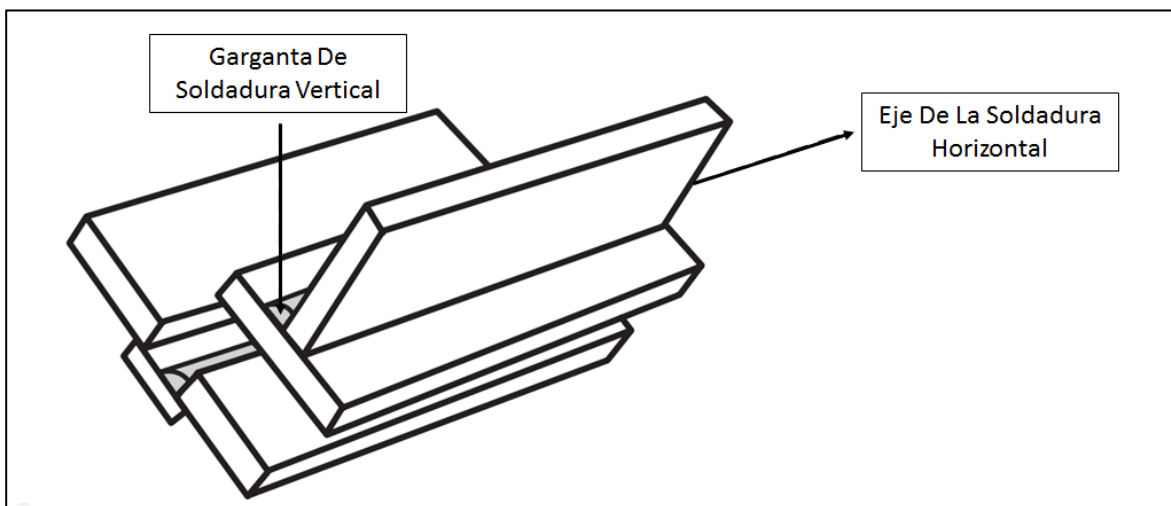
Soldadura De Filete En Posición 1F [58].
